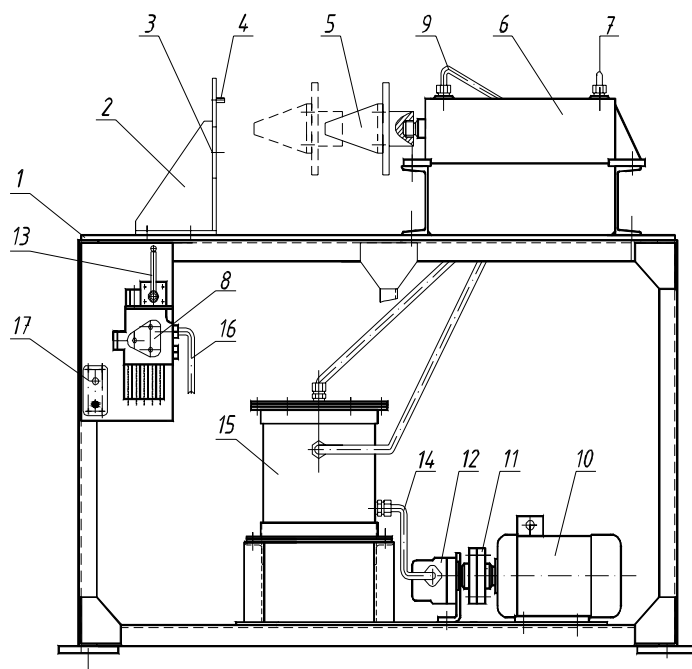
Стенд для разборки и сборки топливных насосов
